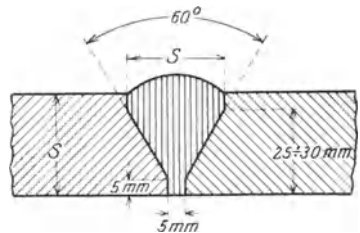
Bearbeitung der Schweißmulde ohne Stiftsetzung.
